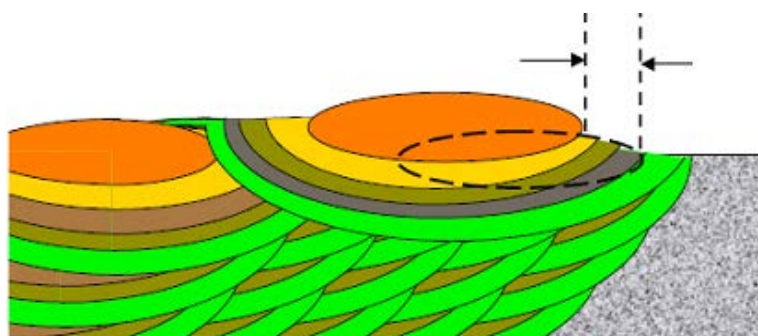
Superfície revenida reforçando a deposição do cordão de solda – Exploring temper bead Welding (Walter J. Sperko – Welding Journal – July – 2005).
